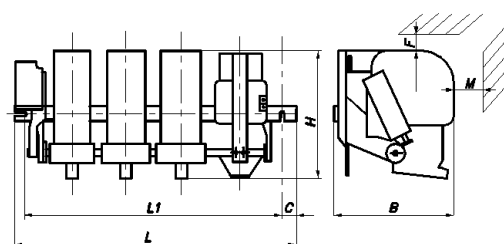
Общий вид и габаритные размеры КТ-5000.
